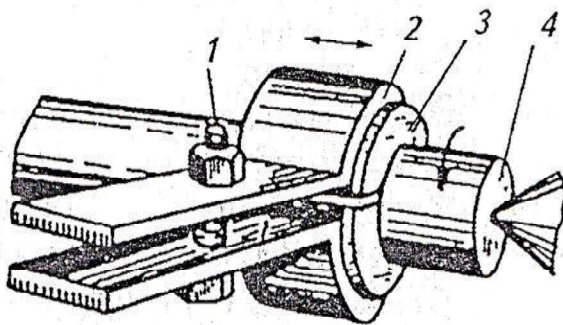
Притирка шейки вала на токарном станке вручную
